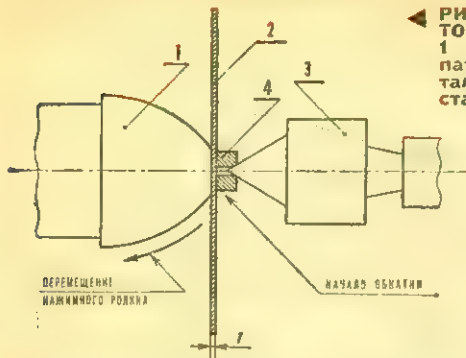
ИЗГОТОВЛЕНИЕ РЕАКТОРА:
